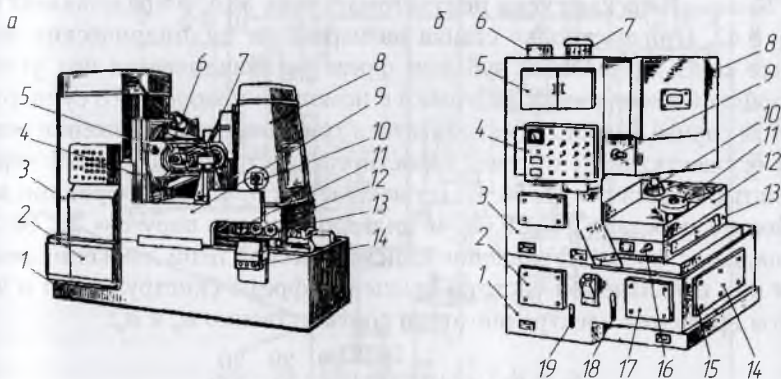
Зубообрабатывающие станки-полуавтоматы:
